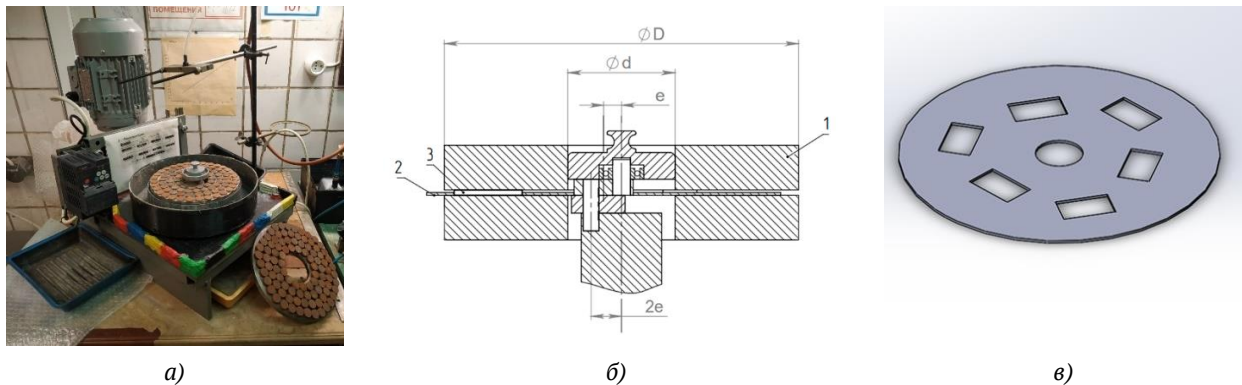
Внешний вид (а), схема (б) и конструкция сепаратора (в) настольного станка для групповой двухсторонней доводки эксцентрикового типа
